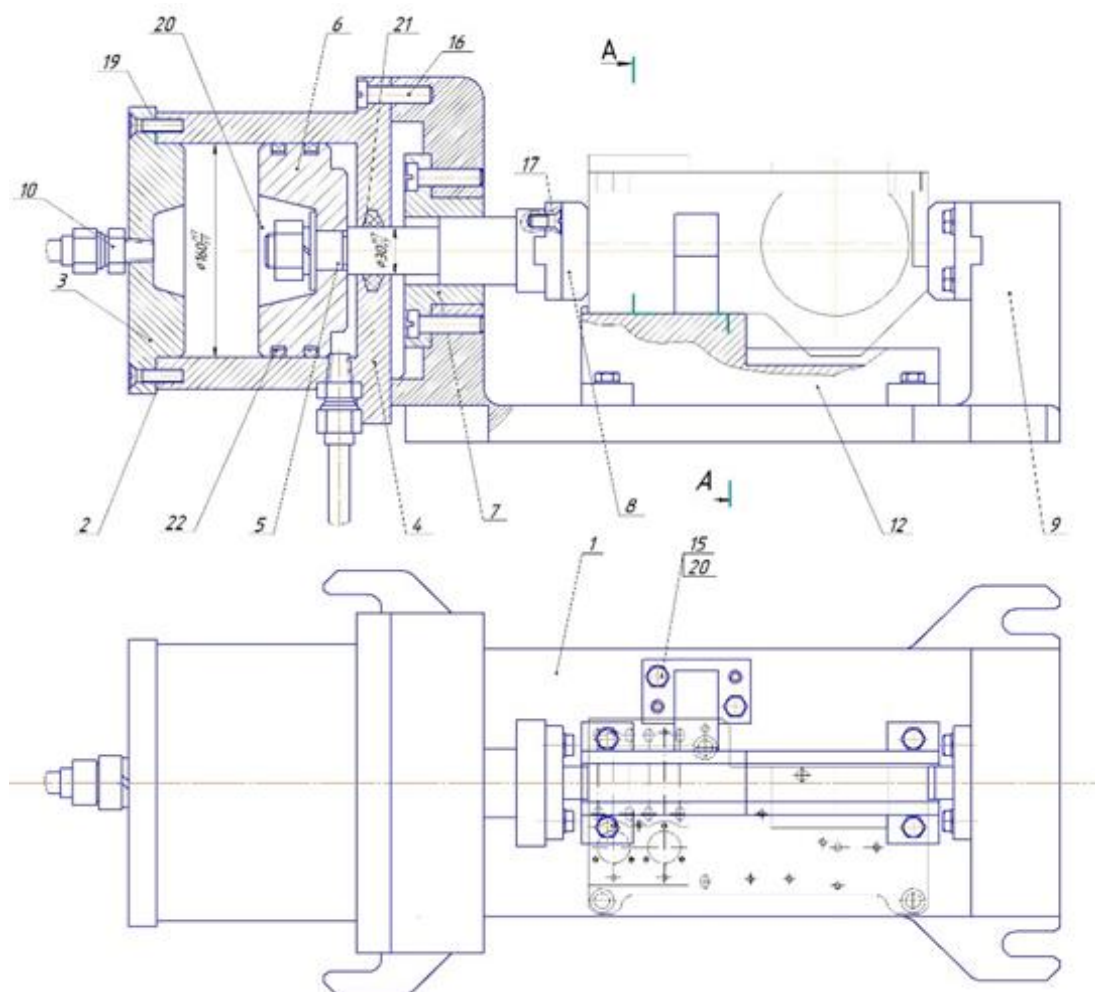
Схема закрепления заготовки в приспособлении
